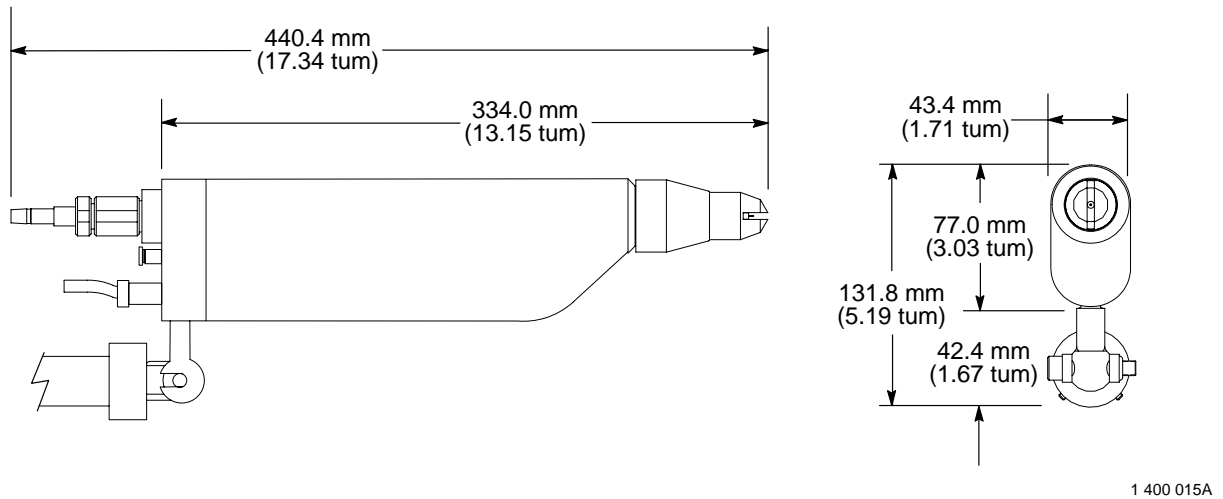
Dimensioner för stångmonterad Sure Coat automatisk pulverpraypistol
